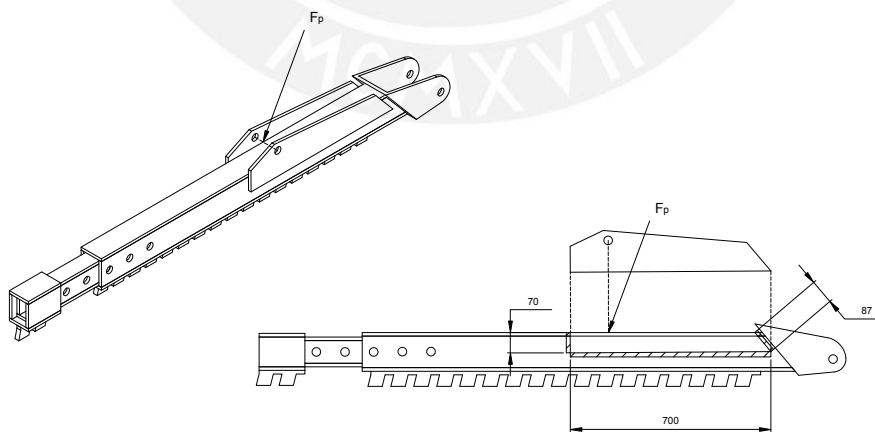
SOLDADURA EN EL SOPORTE DELCILINDRO
